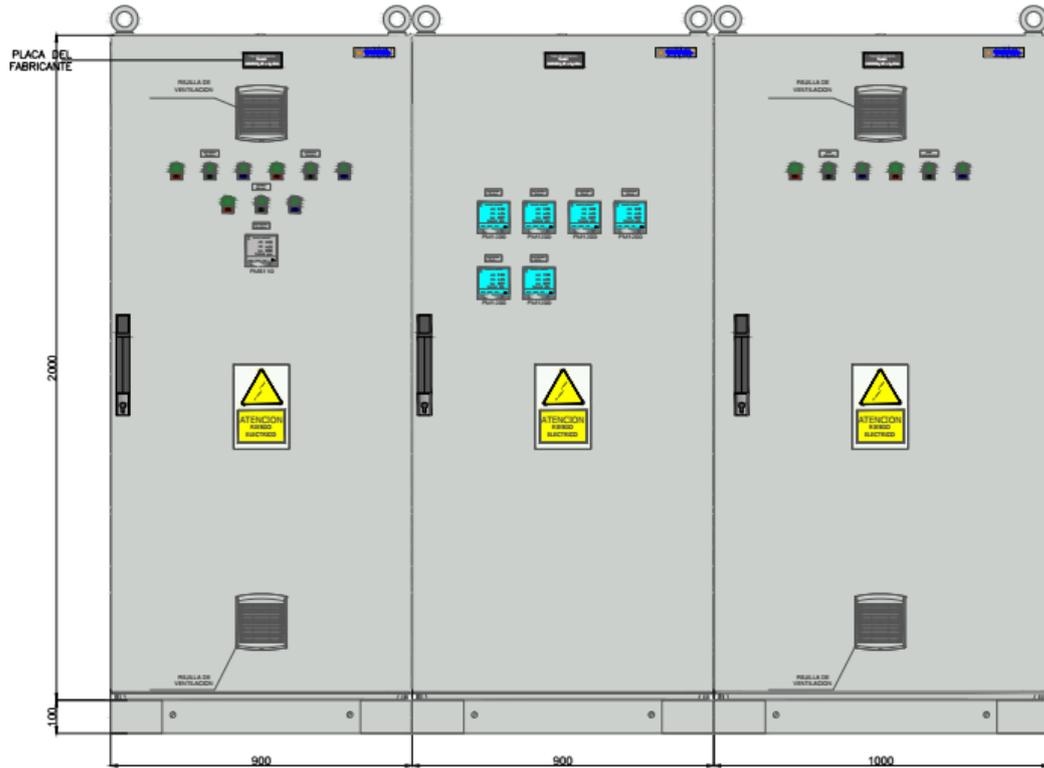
Diseño Mecánico del Tablero en AutoCAD - Vista Frontal.
